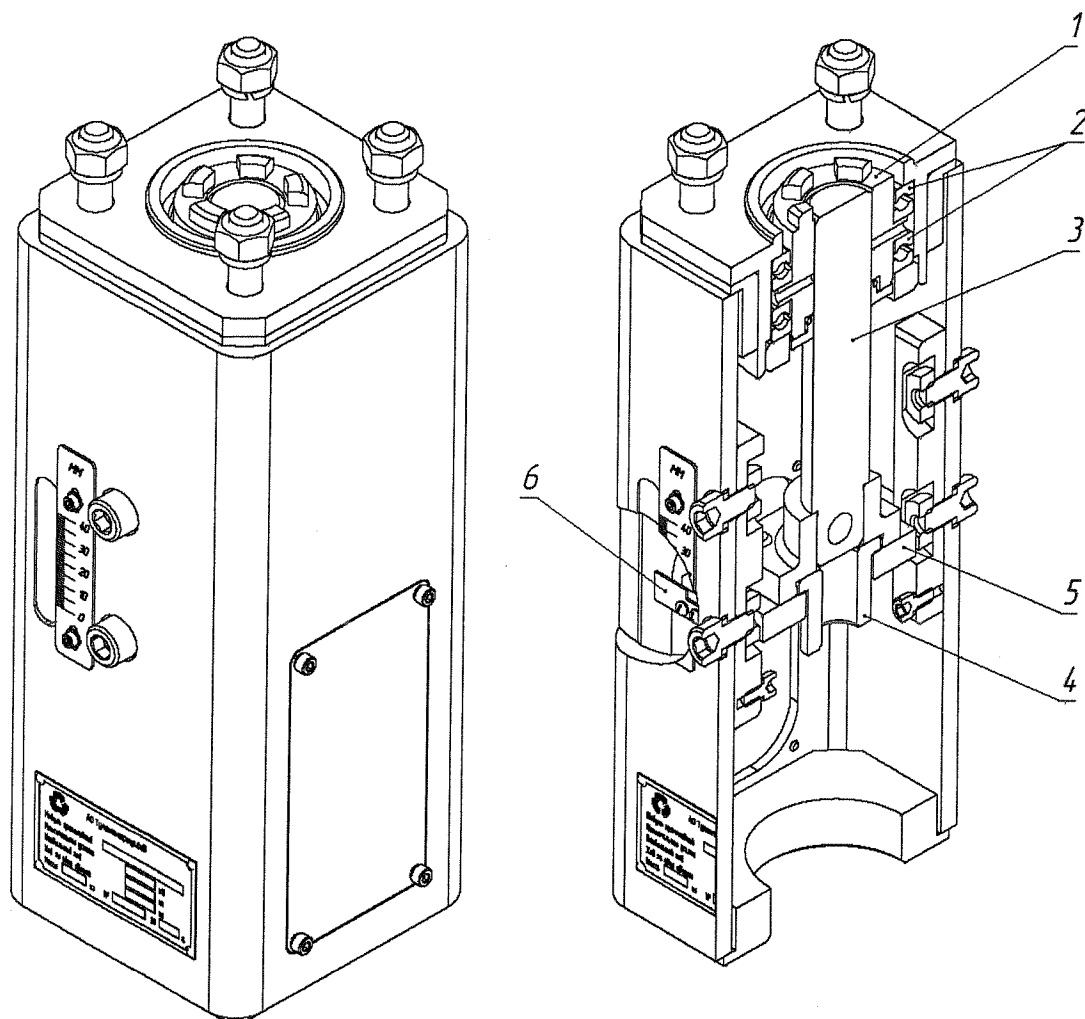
Конструкция модуля (общий вид и разрез)
